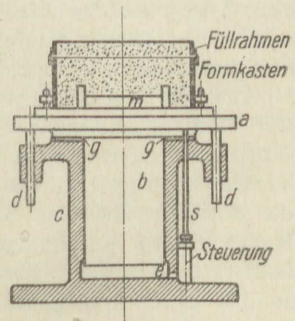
Schema einer Druckluft-Rüttelformmaschine.
